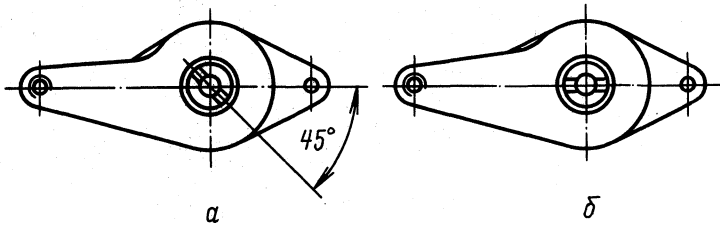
Положения привода прерывателя-распределителя двигателя ЗМЗ-24:
